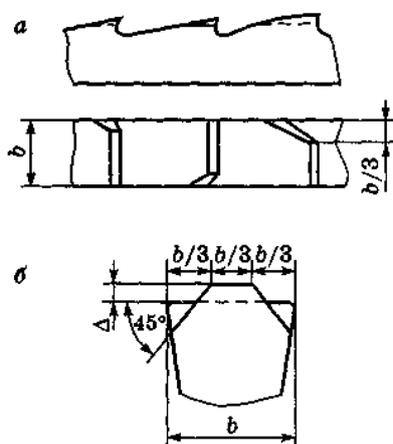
Схемы резания прорезными и отрезными фрезами
